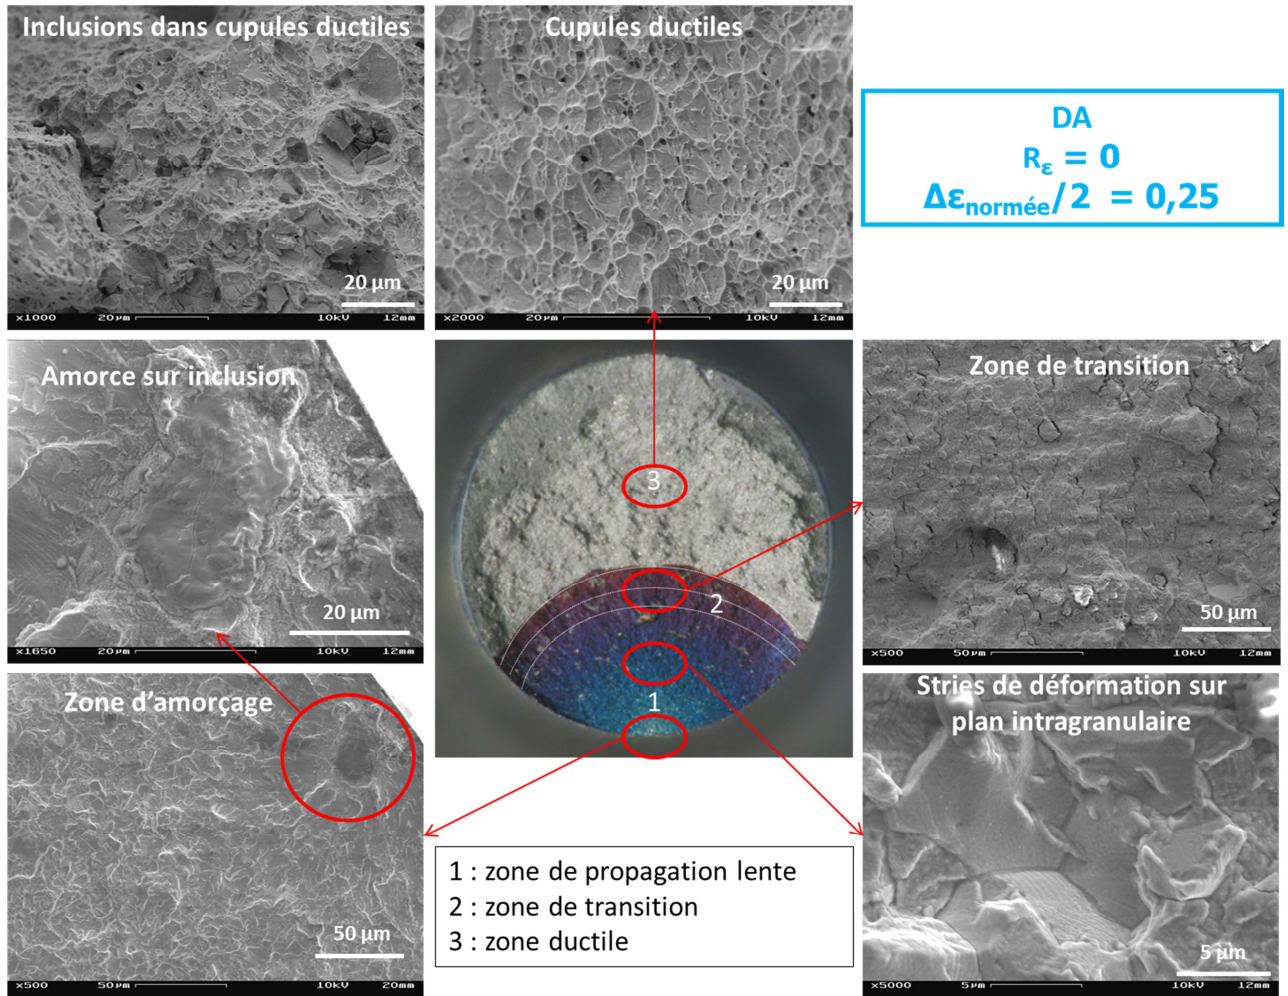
Fractographie type d'une éprouvette en Inconel 718 DA.
